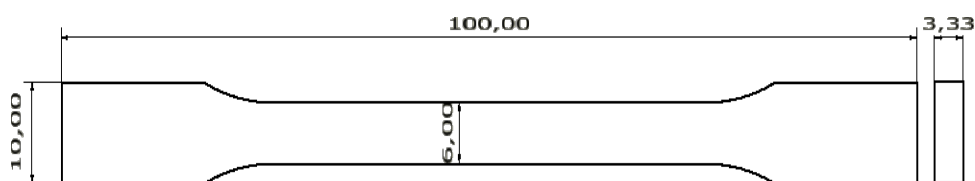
Corpo de prova utilizado para o ensaio de tração. Fonte: Adaptado [5].
